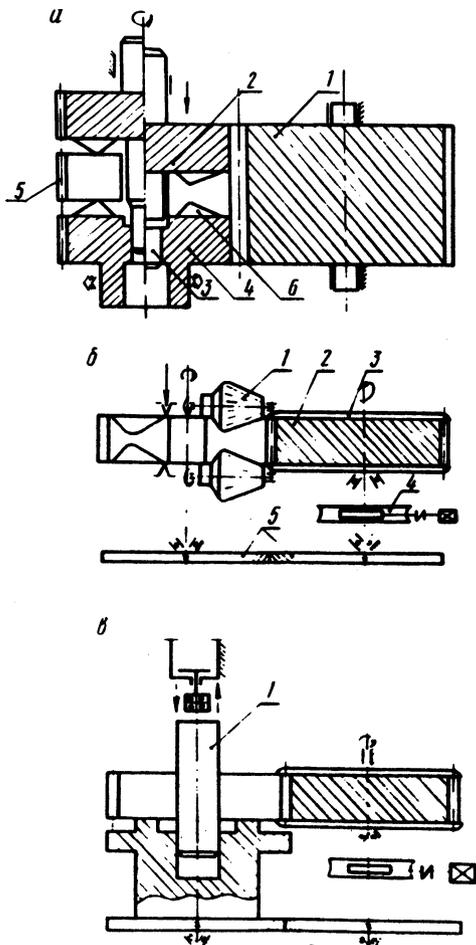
Схемы восстановления зубчатых колес ротационным деформированием: а - зубчатым пуансоном; б - раскатными роликками; в - коническим дорном.
